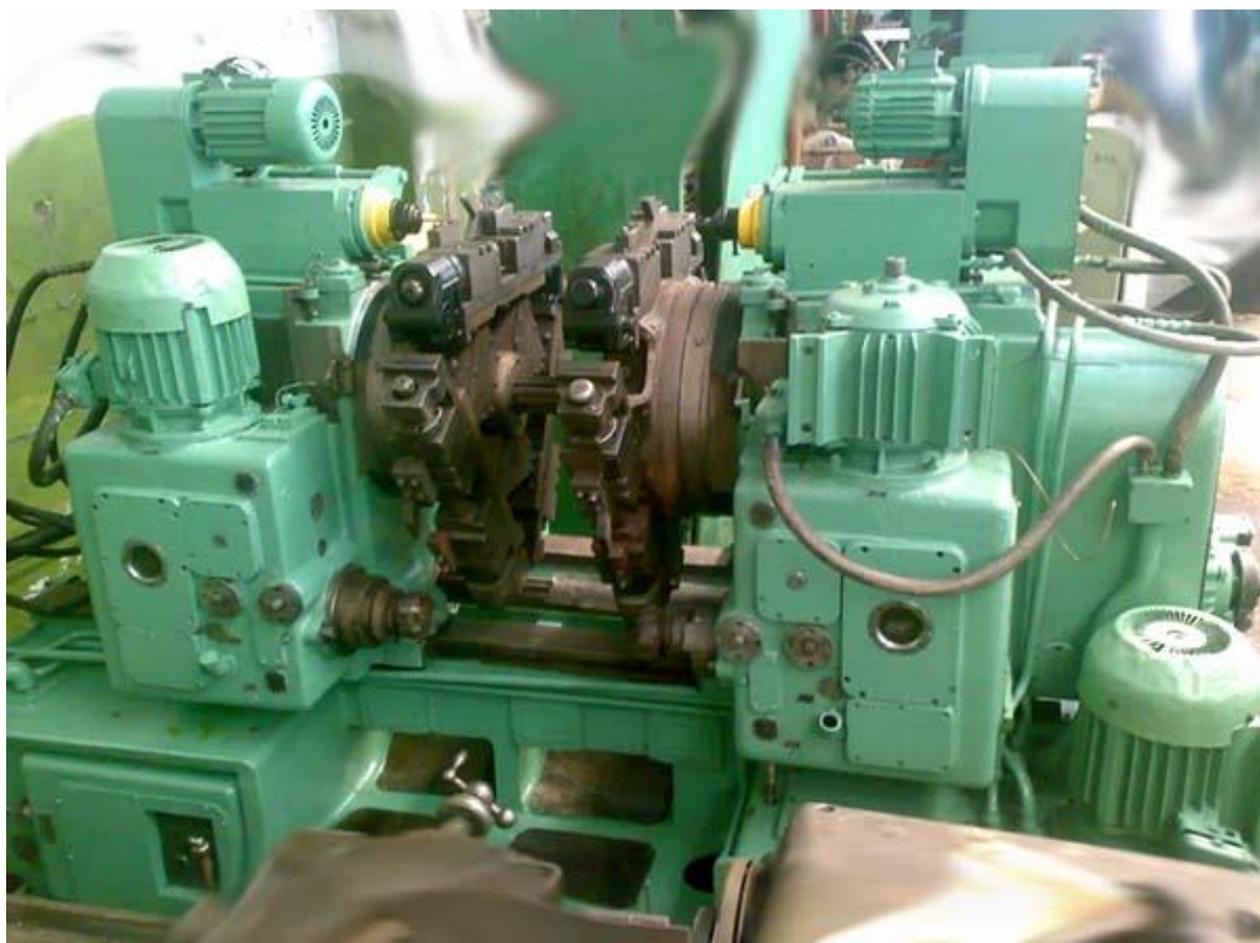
Фрезерно-центровальный станок МР-71М
